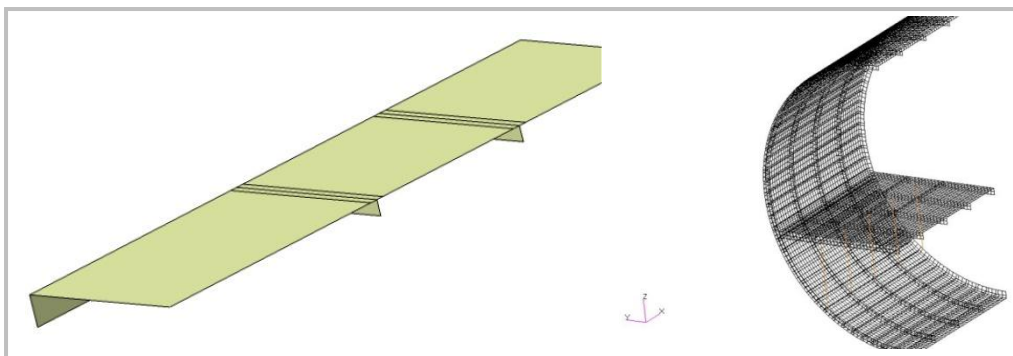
Modellierter Fußboden in CAD (links) Flugzeugrumpf FEM (rechts)
